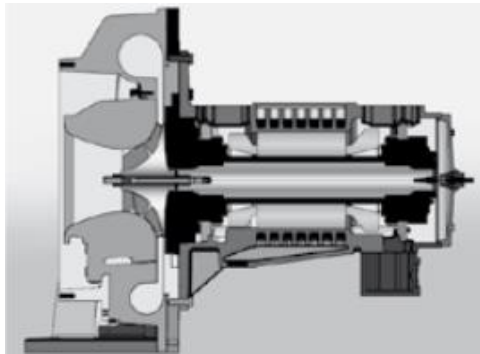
Compresor centrífugo. Fuente: Junta de Castilla y León.
